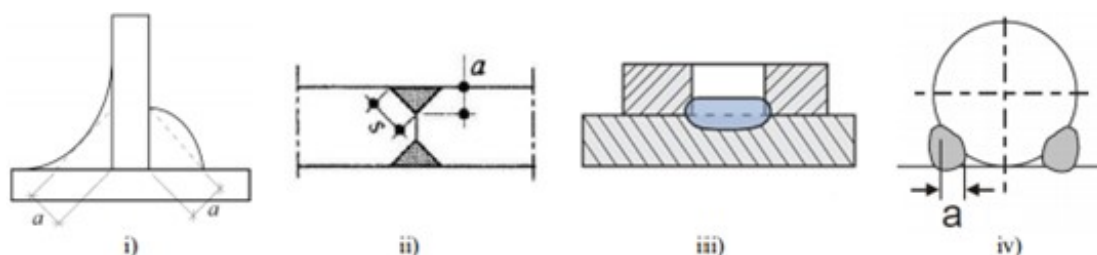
Exemplos de alguns tipos de soldadura abrangidos pelo EC3-1-8 (adaptado de CEN (2010b)).
